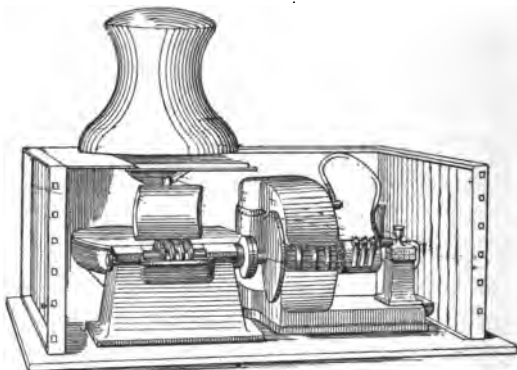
Vue d'ensemble du cabestan électrique de la maison Scott et Mountain.
